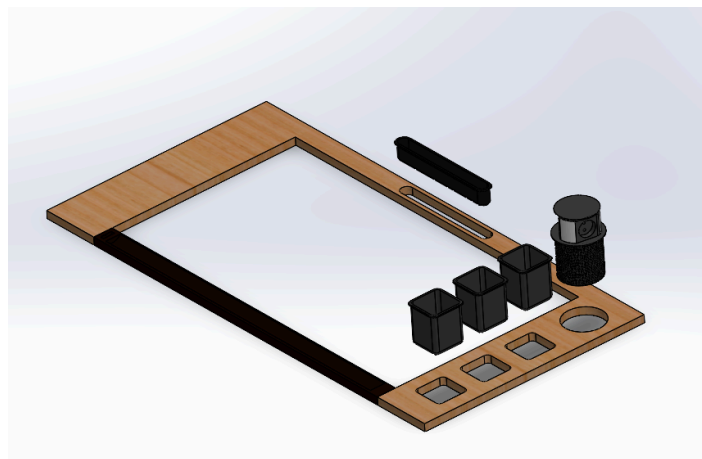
Vista Explosionada de los Complementos del Tablero (Fuente: Elaboración Propia)
